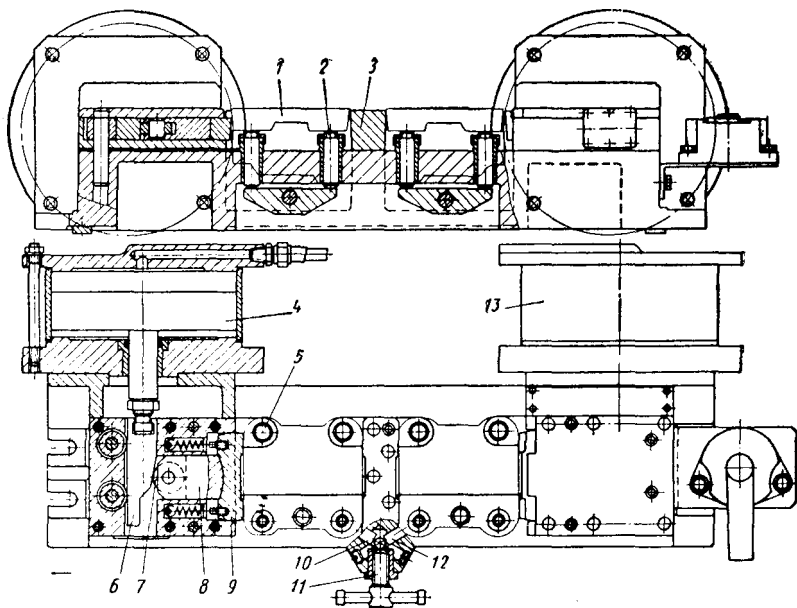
Многоместное фрезерное приспособление с дополнительными опорами
